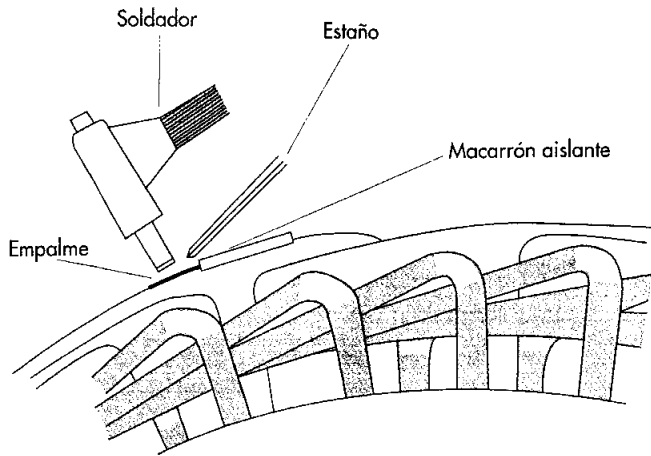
Conexión entre bobinas y entre grupos mediante un soldador.
